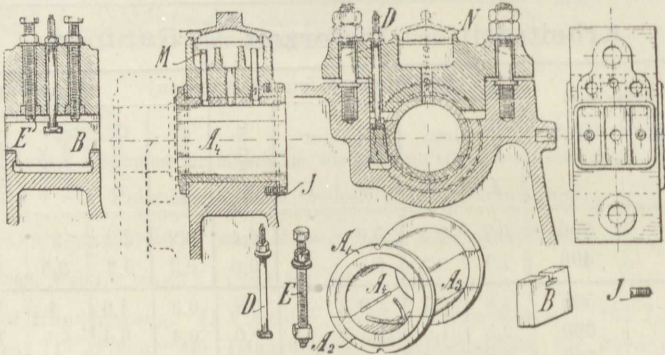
Hauptlager für Maschinen bis 900 Hub.
